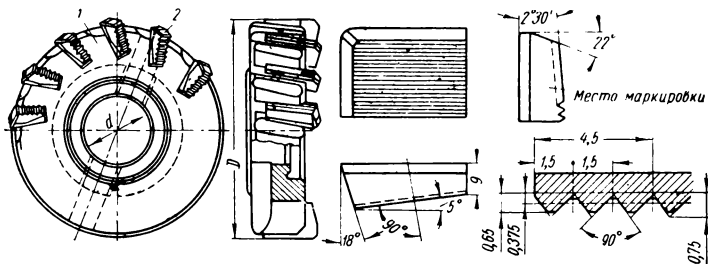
Крепление клиновидных ножей с осевыми рифлями и двойным наклоном в корпусе торцевой фрезы (конструкция по ГОСТу 9473—60):
